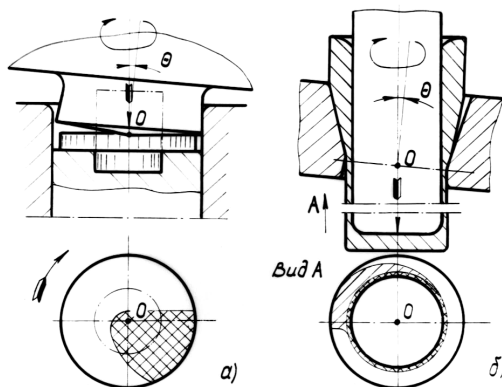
Схема осадки обкатыванием цилиндрической заготовки в штампе – а и вытяжки с утонением стенки в обкатывающей матрице – б
